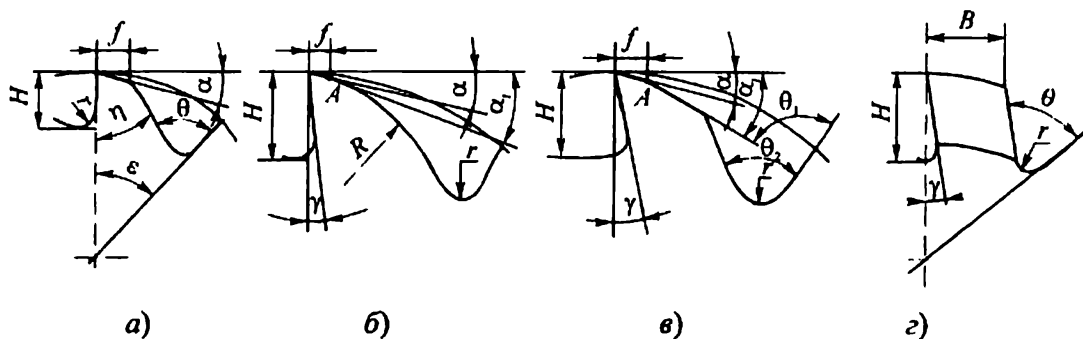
Формы зубьев фрез: *a* – трапецевидные; *б* – параболические; *в* – усиленные; *г* – затылованный зубец
